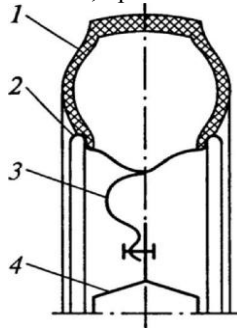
Колесо: 1 - шина; 2 - обід; 3 - з'єднувальний елемент; 4 – маточина.
